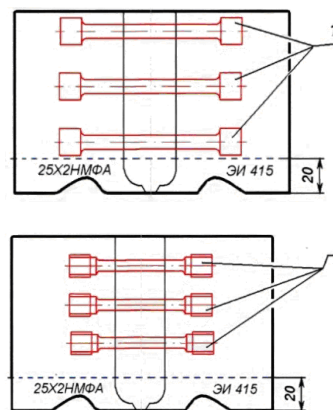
Схема вырезки образцов для испытания на растяжение металла контрольного сварного соединения сталей 25Х2НМФА+ЭИ415:
